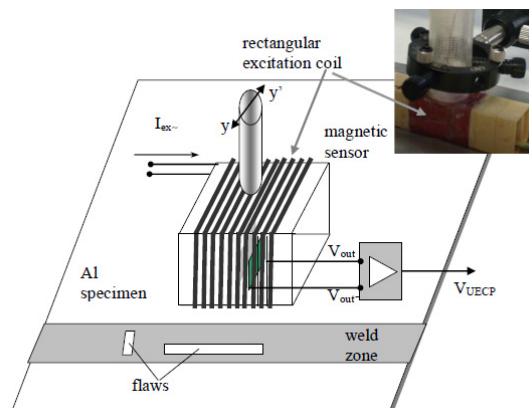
Sonda uniforme de correntes induzidas com GMR sobre uma placa de alumínio com defeitos no cordão de soldadura [20].
